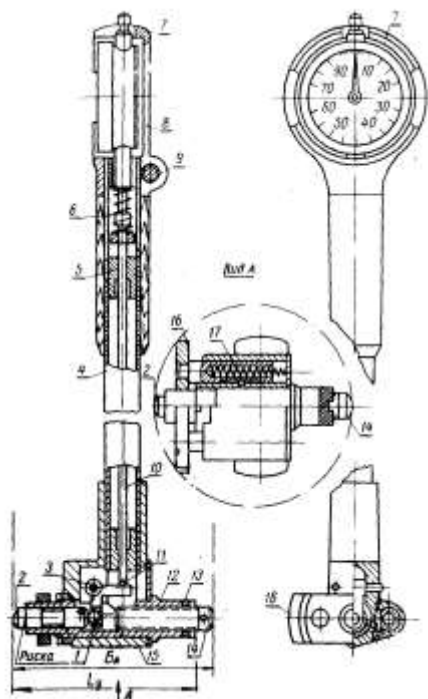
Индикаторный нутромер с рычажной передачей: 1 – шарик; 2 – подвижный стержень; 3 – ось; 4 – трубка; 5 – теплоизоляционная прокладка; 6 – пружина; 7 – кожух; 8 – индикатор; 9 – стопорный винт; 10 – стержень; 11 – двуплечий рычаг; 12 – втулка; 13 – стопорная гайка; 14 – переставной стержень; 15 – корпус; 16 – центрирующий мостик; 17 – пружина
